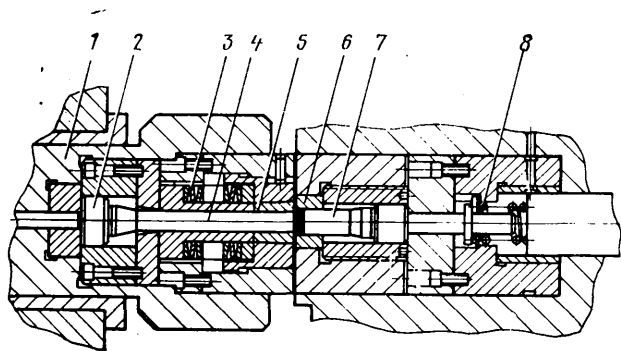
Наладка инструмента к холодновысадочному автомату для поперечного выдавливания заготовок
